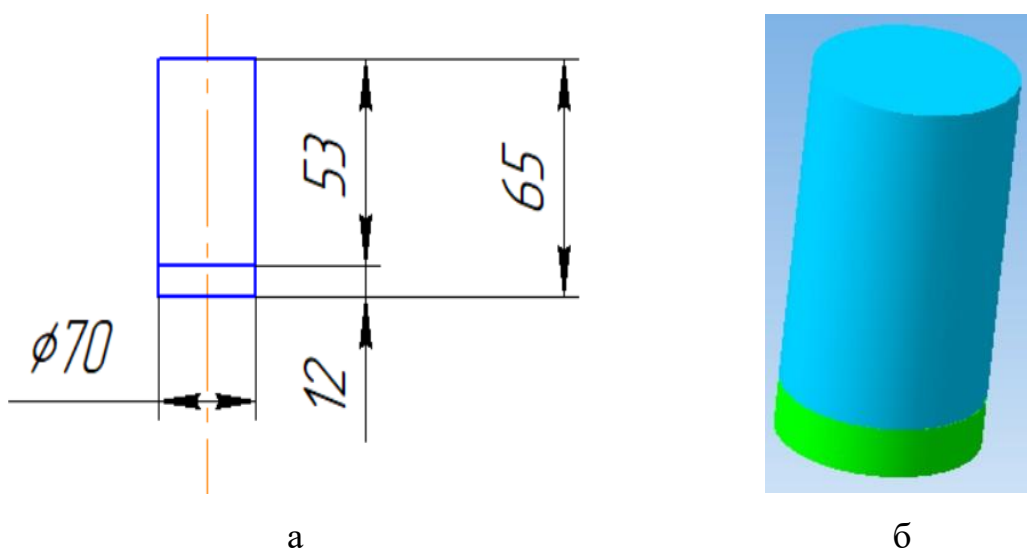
Вихідна заготовка: а – ескіз біметалевої заготовки; б – 3D-модель заготовки.
